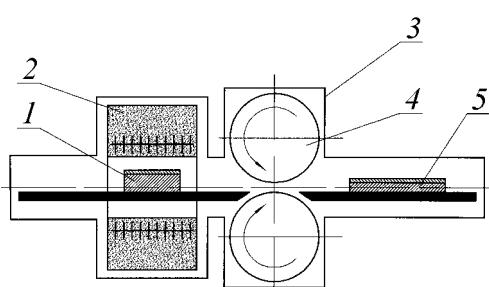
Схема вакуумной прокатки пакета: 1 – пакет до прокатки, 2 – печь, 3 – вакуумная камера, 4 – валки прокатного стана, 5 – монолитная заготовка после прокатки
